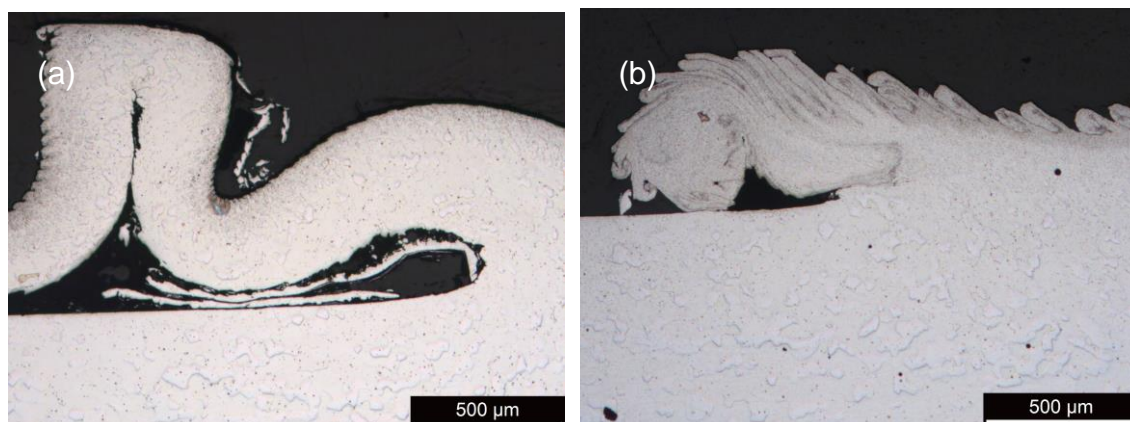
Macrografias da seção transversal das diferentes condições soldadas do aço AISI 444.
